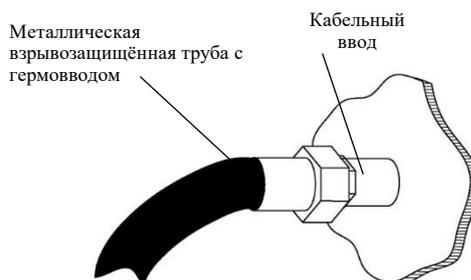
Соединение металлической взрывозащищённой трубы и камеры
